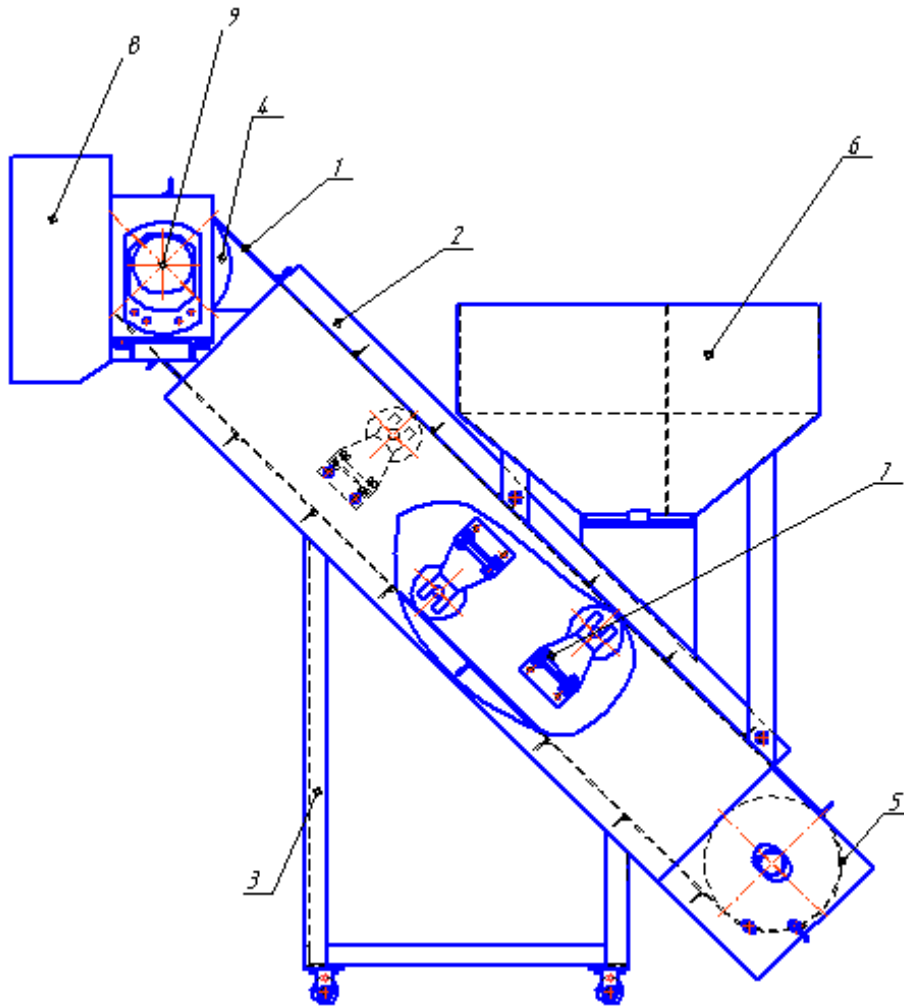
Ленточно-скребковый питатель: 1 – лента со скребками; 2 – кожух; 3 – передвижная рама; 4 – приводной барабан; 5 – натяжной барабан; 6 – загрузочный бункер; 7 – ролико-опоры; 8 – направляющий кожух; 9 – мотор-редуктор.
